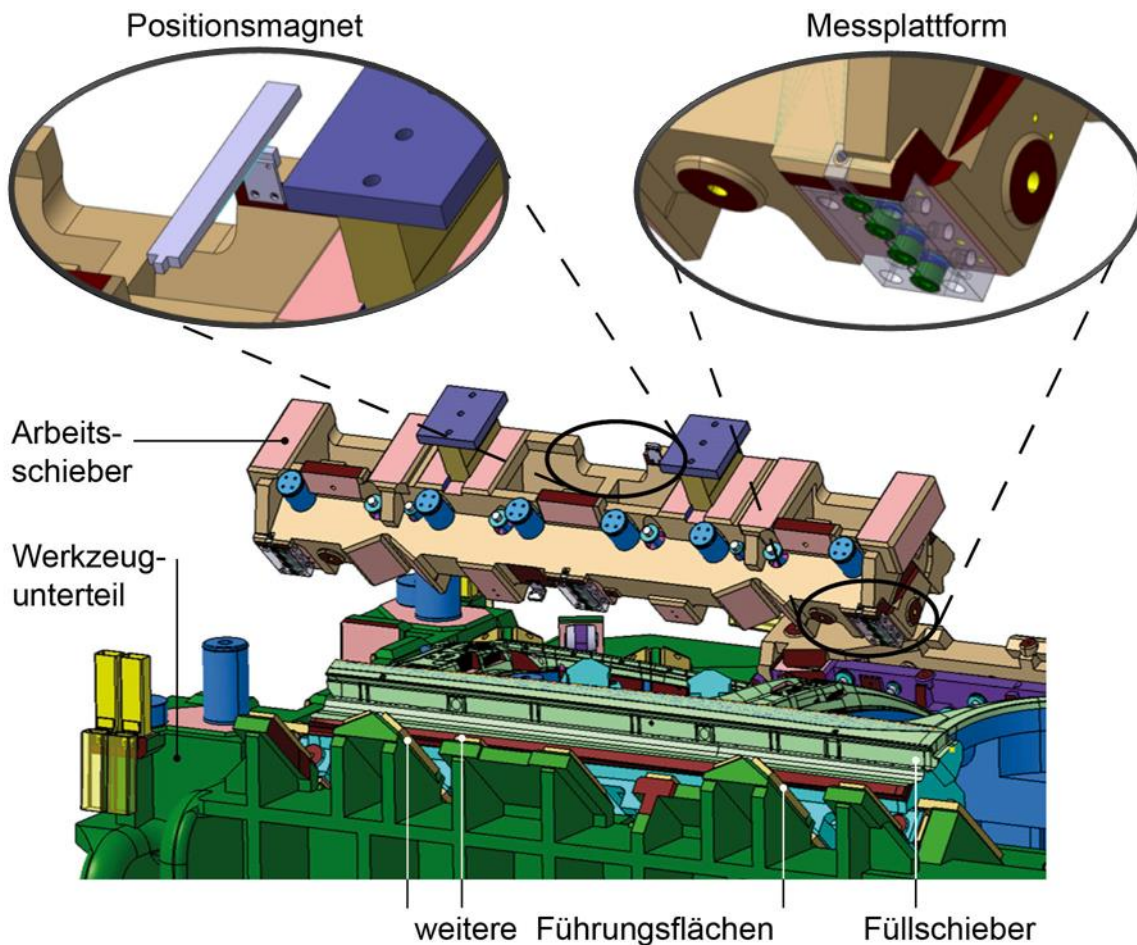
Messaufbau am Schwellerschieber des Seitenwandrahmen-Werkzeugs OP50 des Audi A3 Sportbacks
